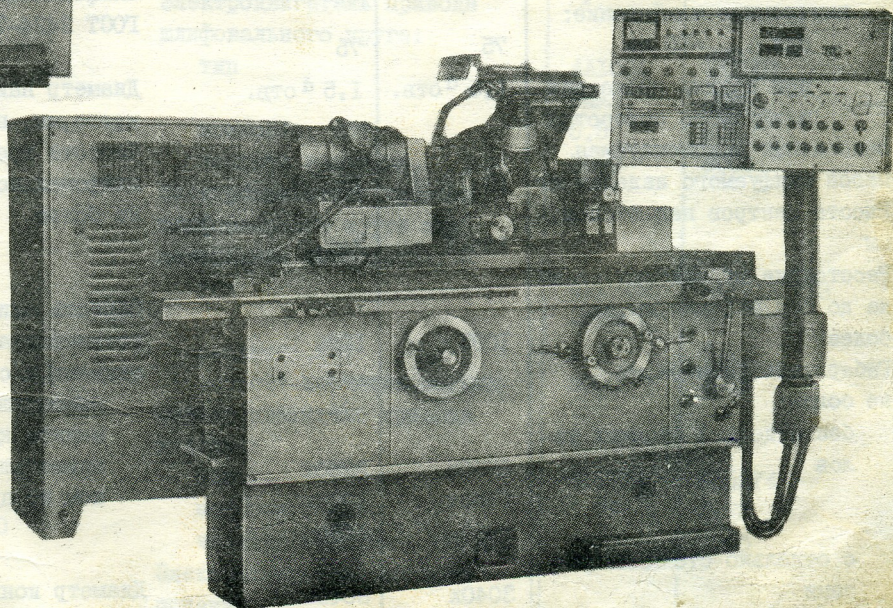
Станок универсальный круглошлифовальный ЗУ12ВФ11
